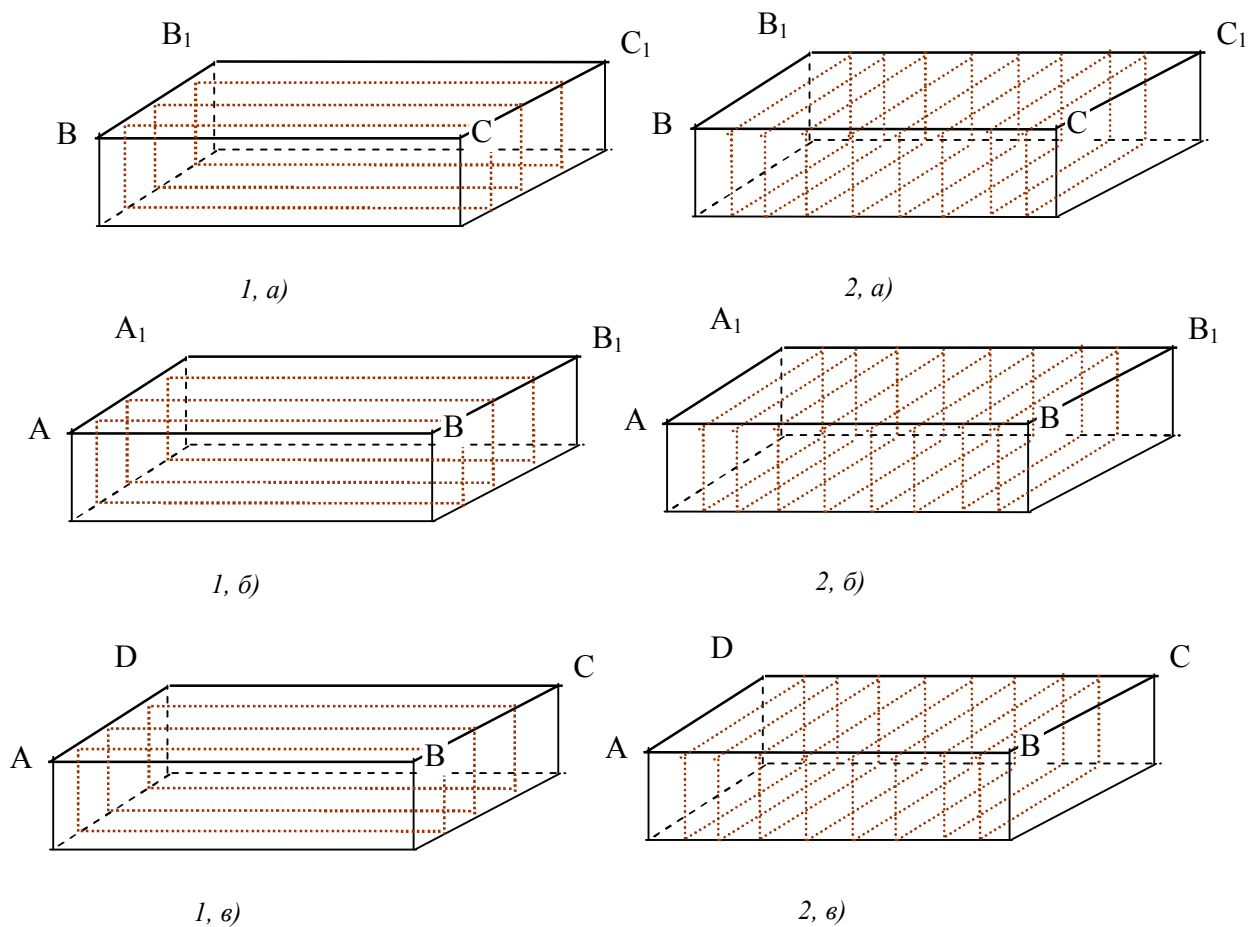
Схеми розпилювання великоформатних заготовок на менші заготовки
